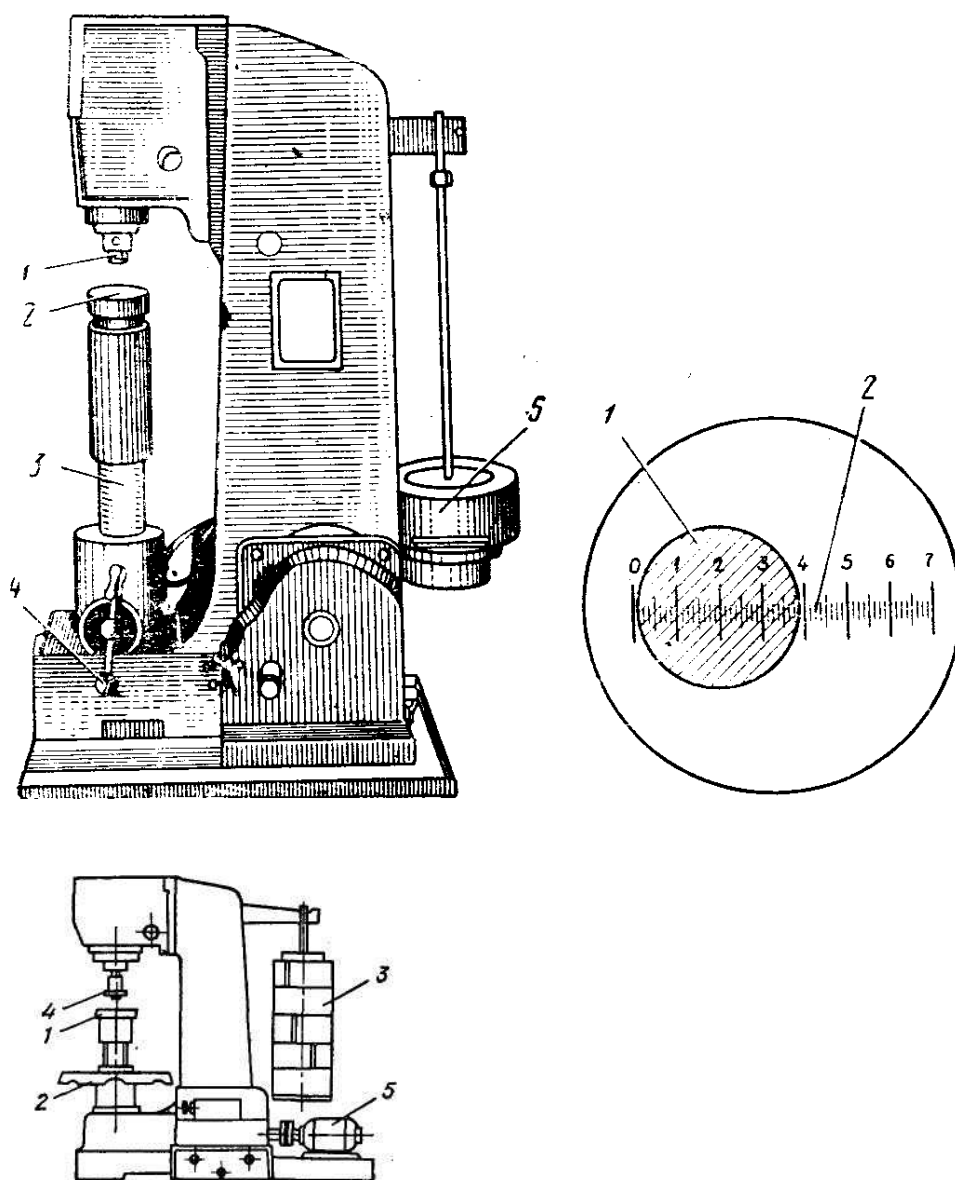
Схема прибора для получения твердости вдавливанием шарика (измерение по Бринеллю): 1 – столик для центровки образца; 2 — маховик; 3 — грузы; 4 — шарик; 5 — электродвигатель.
